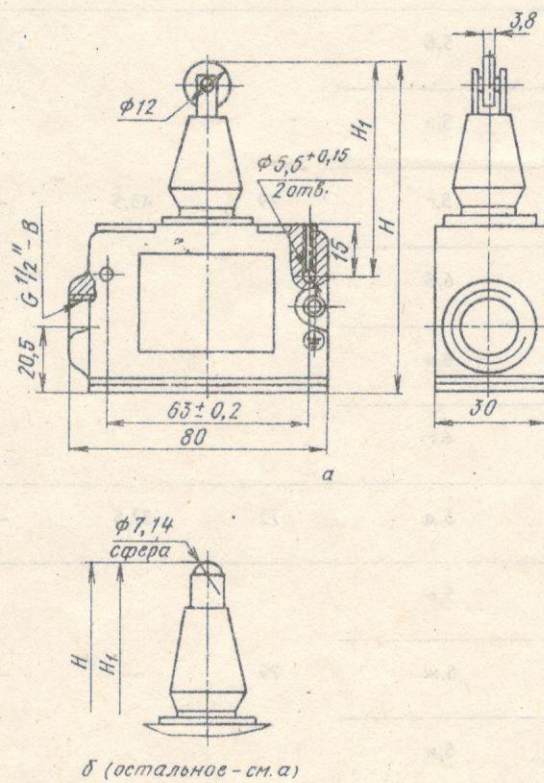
Габаритные, установочные и присоединительные размеры микровыключателей со степенью защиты IP54 с комбинированным креплением на поверхности, с монтажом проводов винтами или пайкой, с приводом
